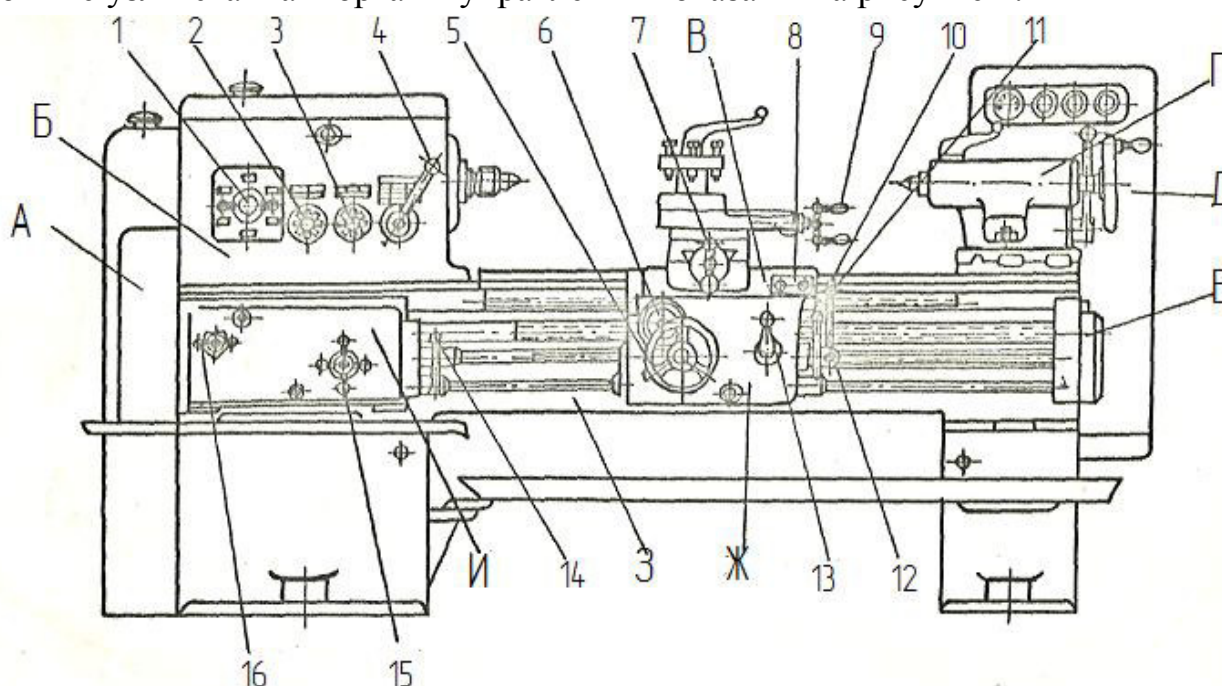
А – гитара сменных колёс; Б – передняя бабка с коробкой скоростей; В – каретка; Г – задняя бабка; Д – шкаф с электрооборудованием; Е – привод ускоренных перемещений; Ж – фартук; З – станина; И – коробка подач.
